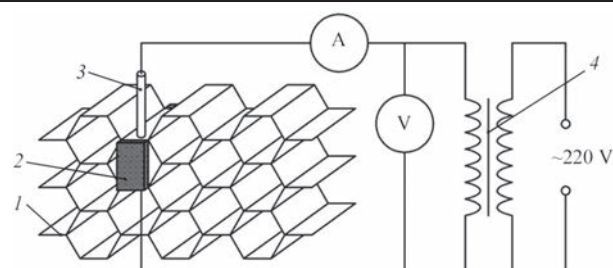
Схема устройства для сварки сотового заполнителя из сплава Ni–Cr: 1 — профилированные ленты; 2 — электрод из графита; 3 — электрод из меди; 4 — трансформатор
